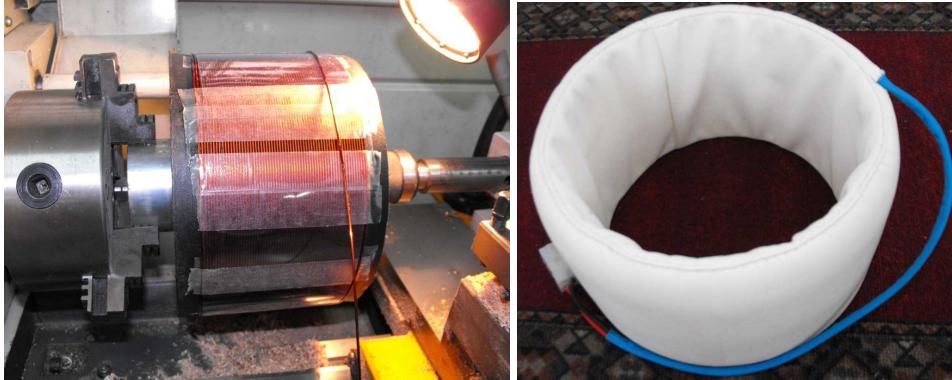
Bobina cilíndrica durante a bobinagem e pronta a usar
